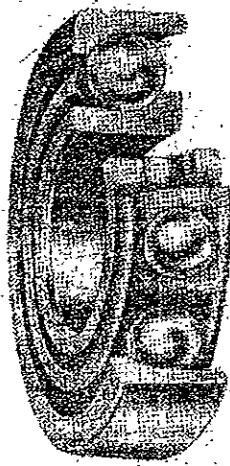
COJINETE DE BOLAS DE CONTACTO ANGULAR
